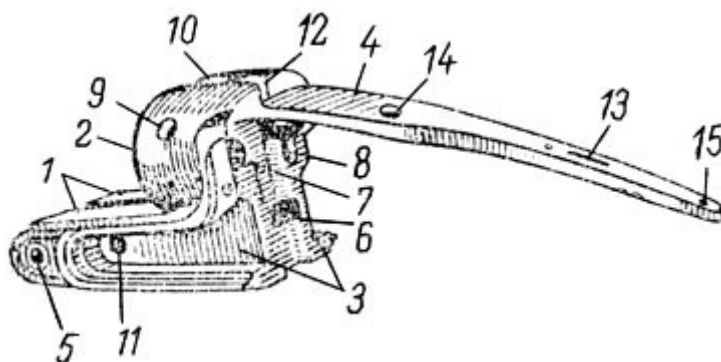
Коленчатая колодка двуствольного ружья с горизонтально-спаренными стволами: 1 — подушка; 2 — лобовой щиток; 3 — гнезда для замков; 4 — хвостовик для крепления с ложей; 5 — осевой шарнирный болт; 6 — паз для затворной рамки; 7 — гнездо инертного бойка; 8 — гнездо пружины затвора; 9 — гнездо для поперечного болта; 10 — гнездо для продолжения прицельной планки; 11 — гнездо для оси взводителя; 12 — отверстие под ось затвора — мотыля; 13 — окно для монтажа кнопкишибера предохранителя; 14 — отверстие для винта упора; 15 — отверстие с резьбой для хвостового винта
